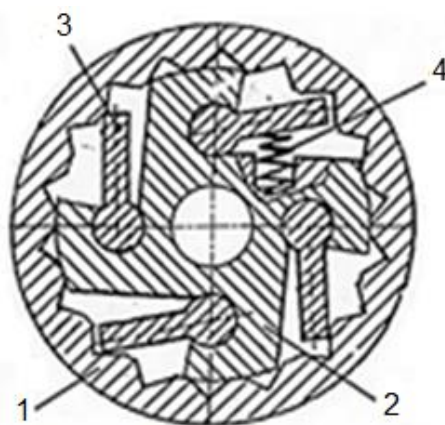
Поворотный механизм с четырьмя собачками в корпусе
